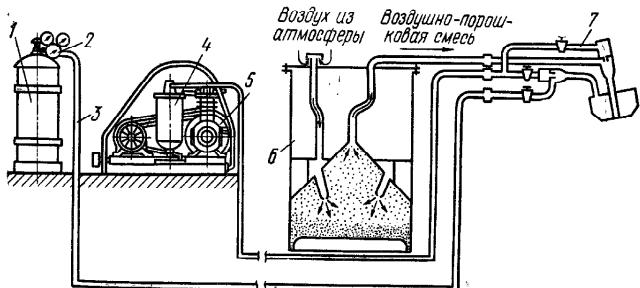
Передвижная установка для газопламенного нанесения цинкового покрытия:
